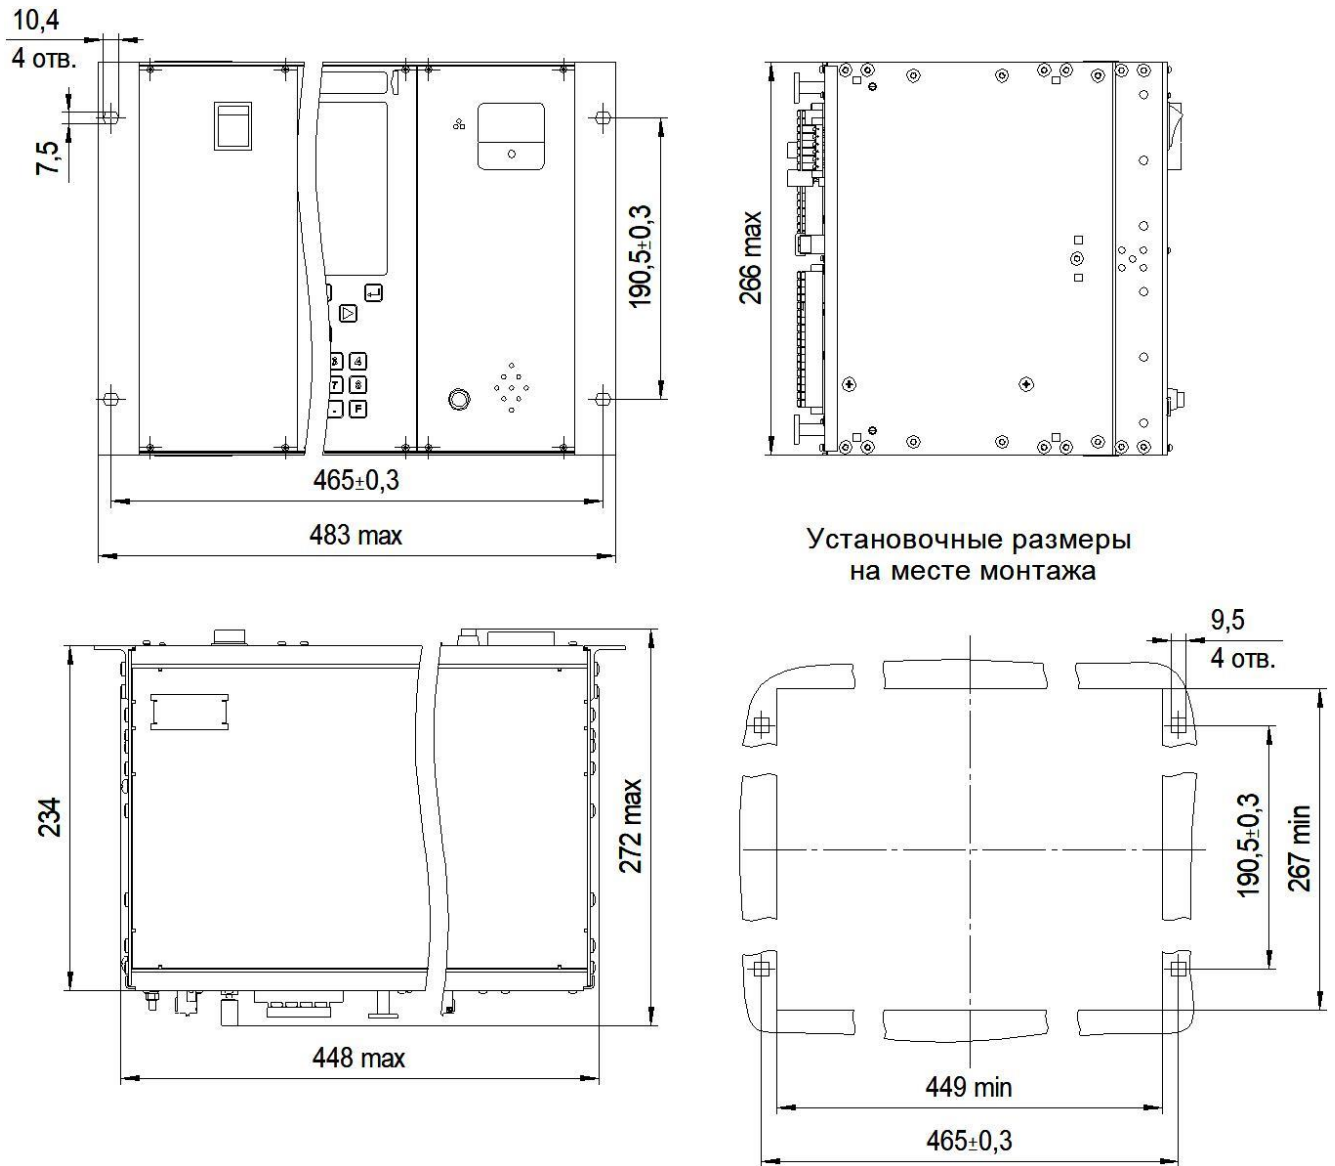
Общий вид, габаритные и установочные размеры терминала
